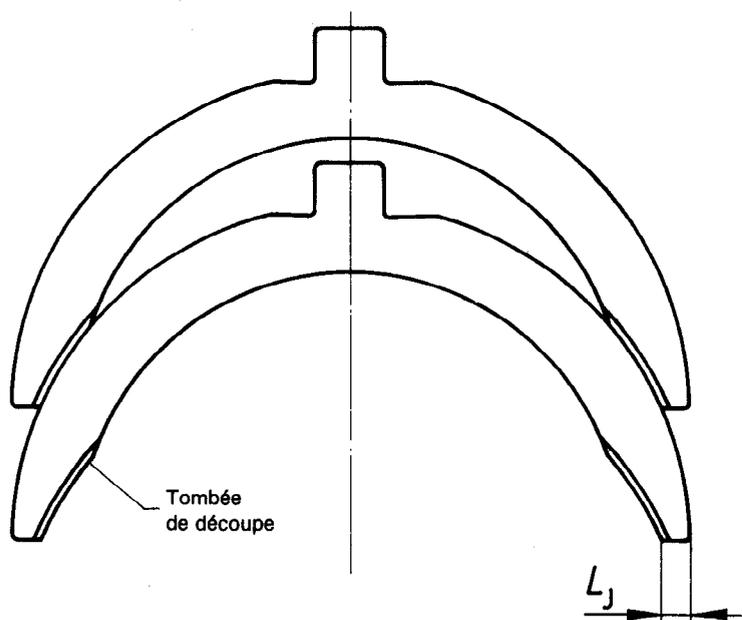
Tombée de découpe des flasques à découpe imbriquée
